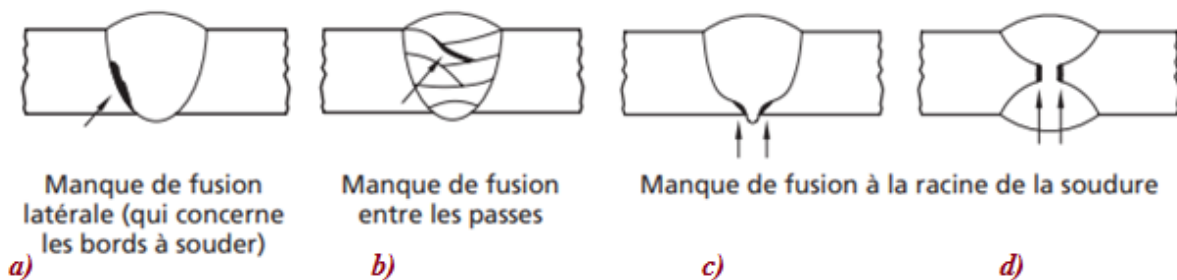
Défauts de collage ou manque de fusion dans une soudure (Réf.[R15])
